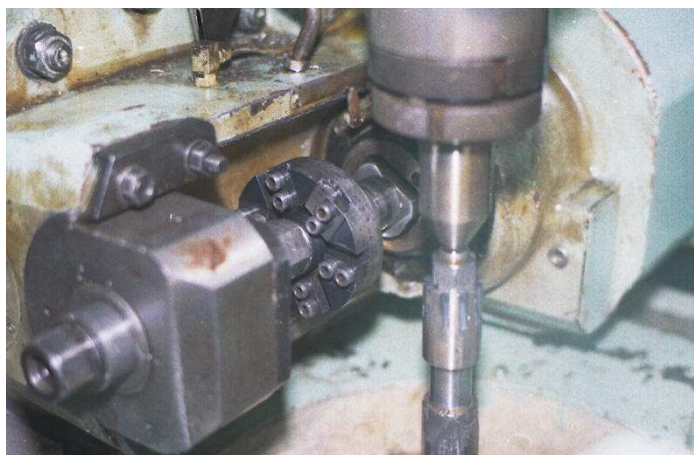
Установка резцовой головки на зубофрезерном станке модели 5B312 при обработке зубчатого контура на наружной поверхности
